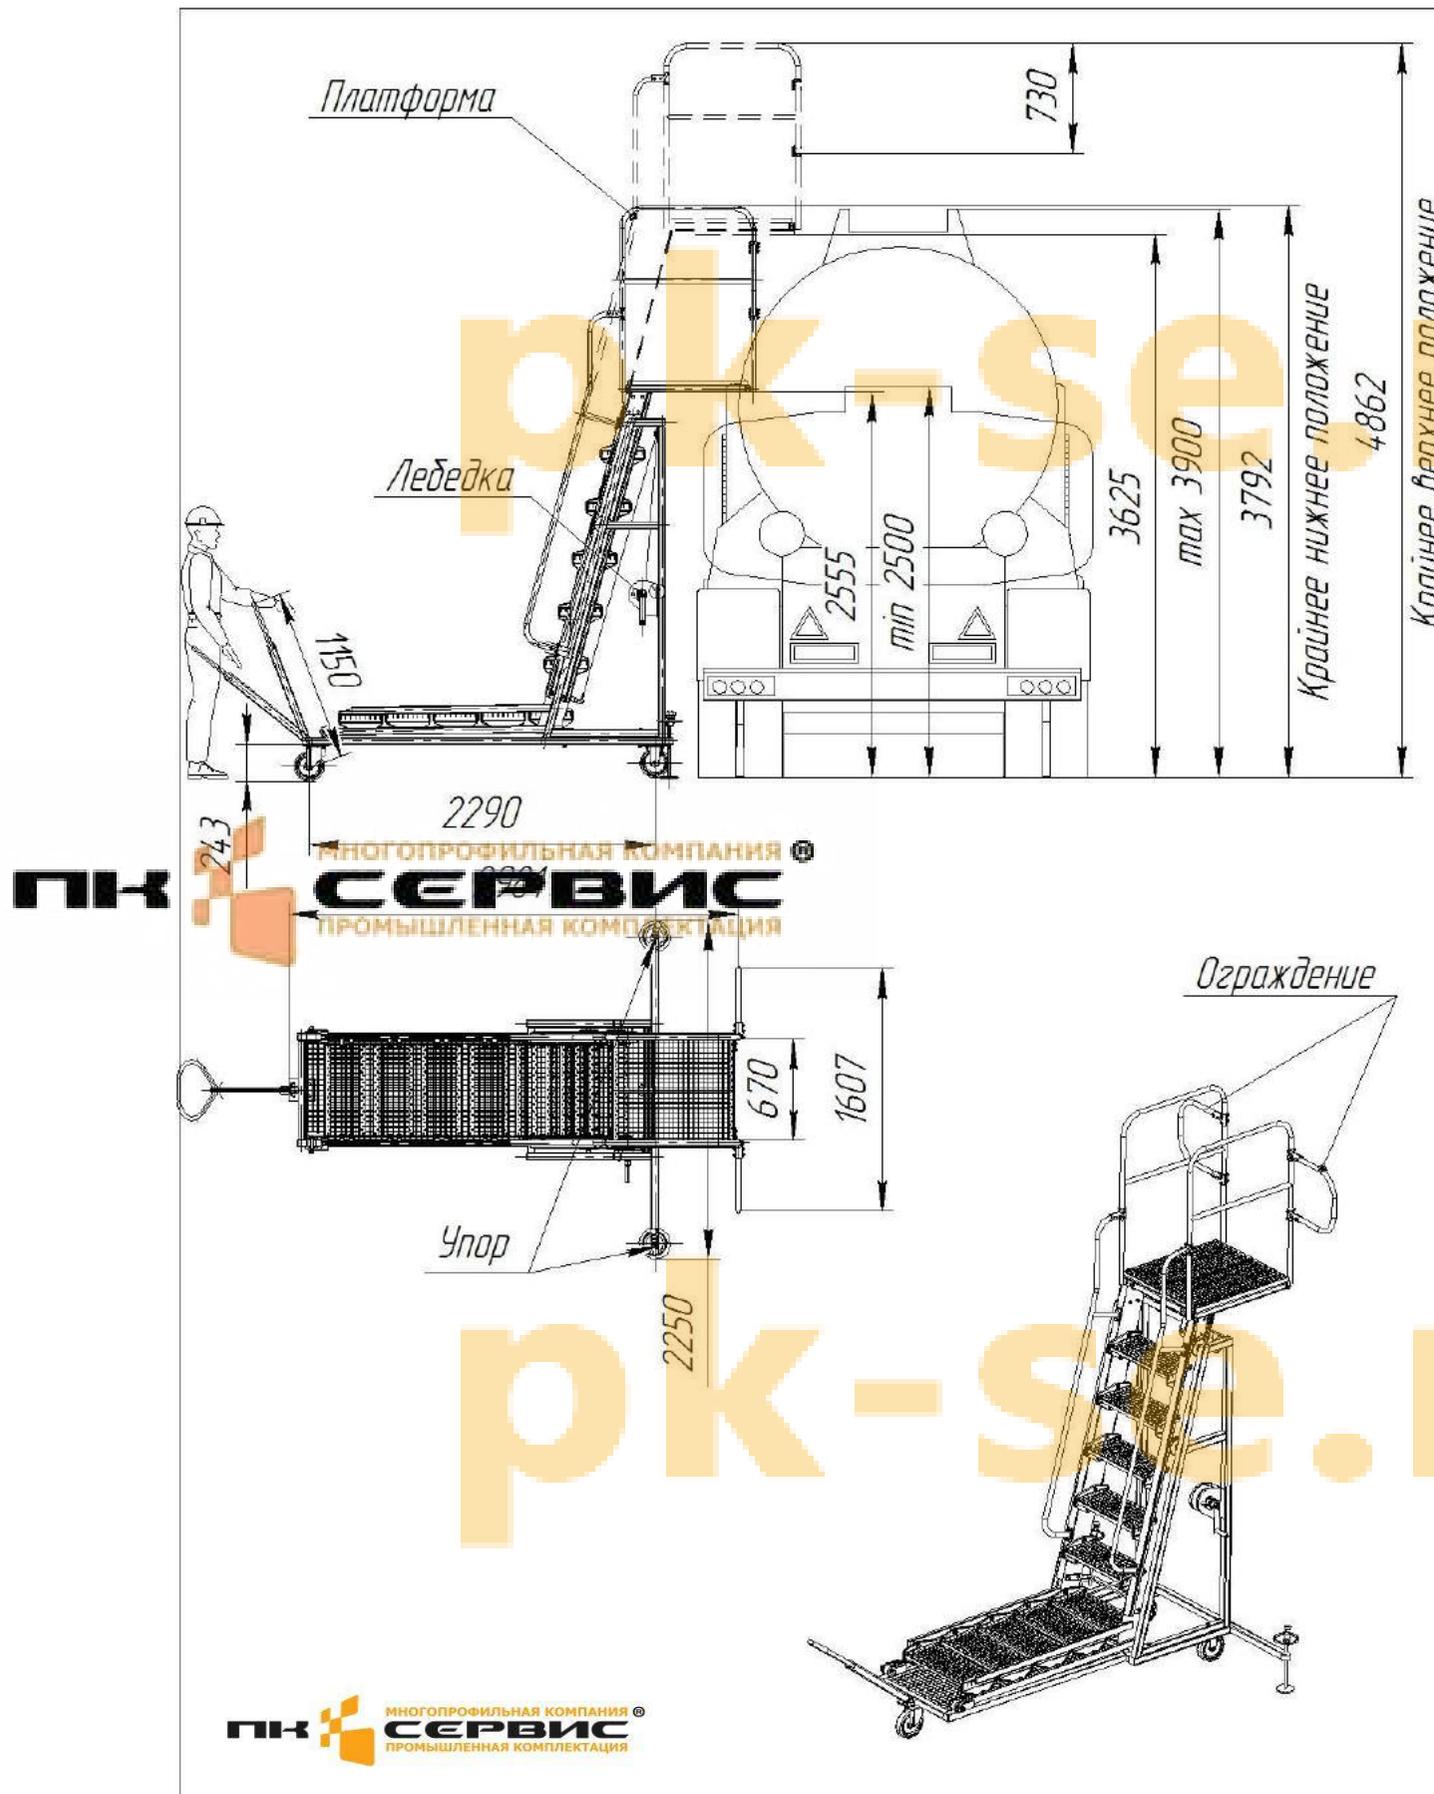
Общий вид, габаритные и присоединительные размеры лестницы передвижной 1220.00.00.00.00-01
